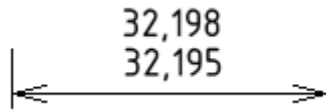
Zápis dĺžkových tolerancií tolerančnými značkami
